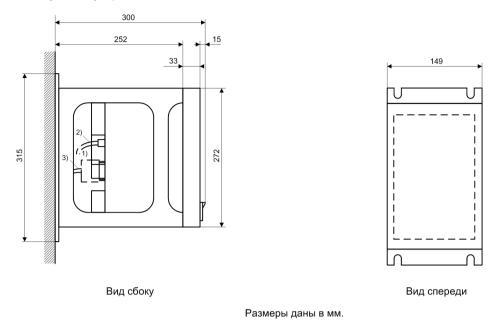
Схема сверления отверстий для устройства навесного монтажа 1/1, второй ряд устройств
